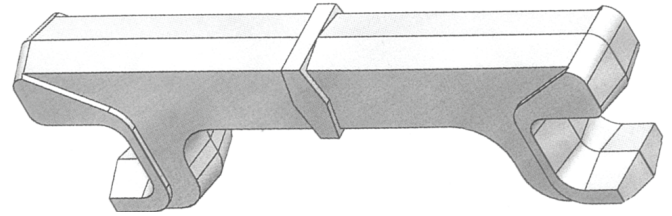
Колосник с дополнительными выступами на боковой поверхности [9]
